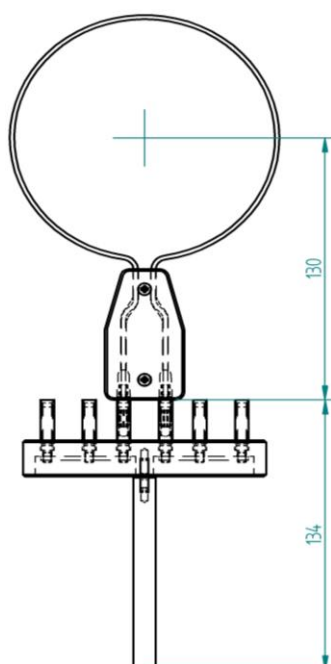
Dimensioni dei conduttori ad anello montati sull'asta di supporto per elementi a spina (1018449)
